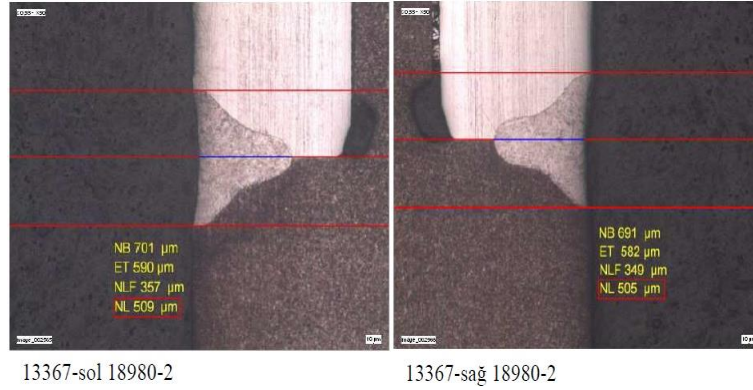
27 0.906 m/dk kaynak hızındaki kaynak dikişi sol ve sağ bölgeleri
